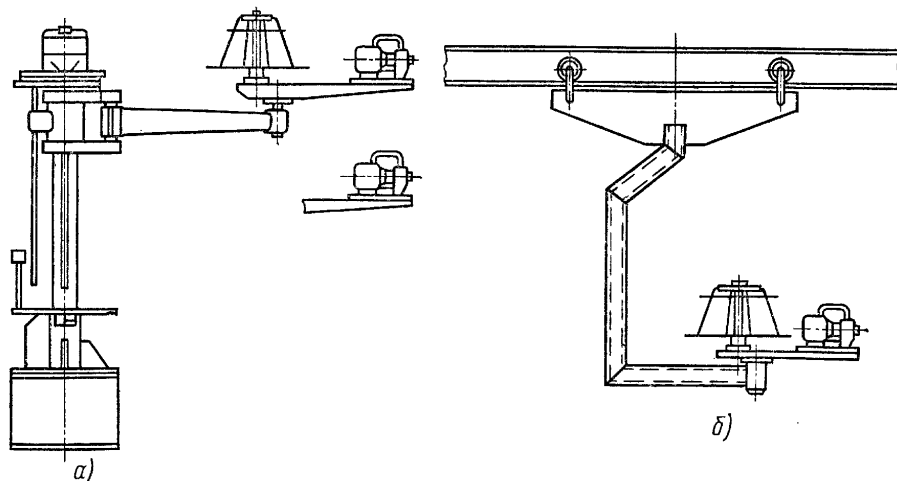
Оборудование для перемещения сварочных полуавтоматов:
